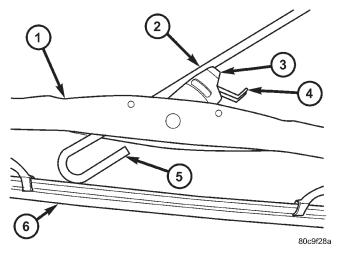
Desmontaje e instalación de escobilla de limpiador delantero
